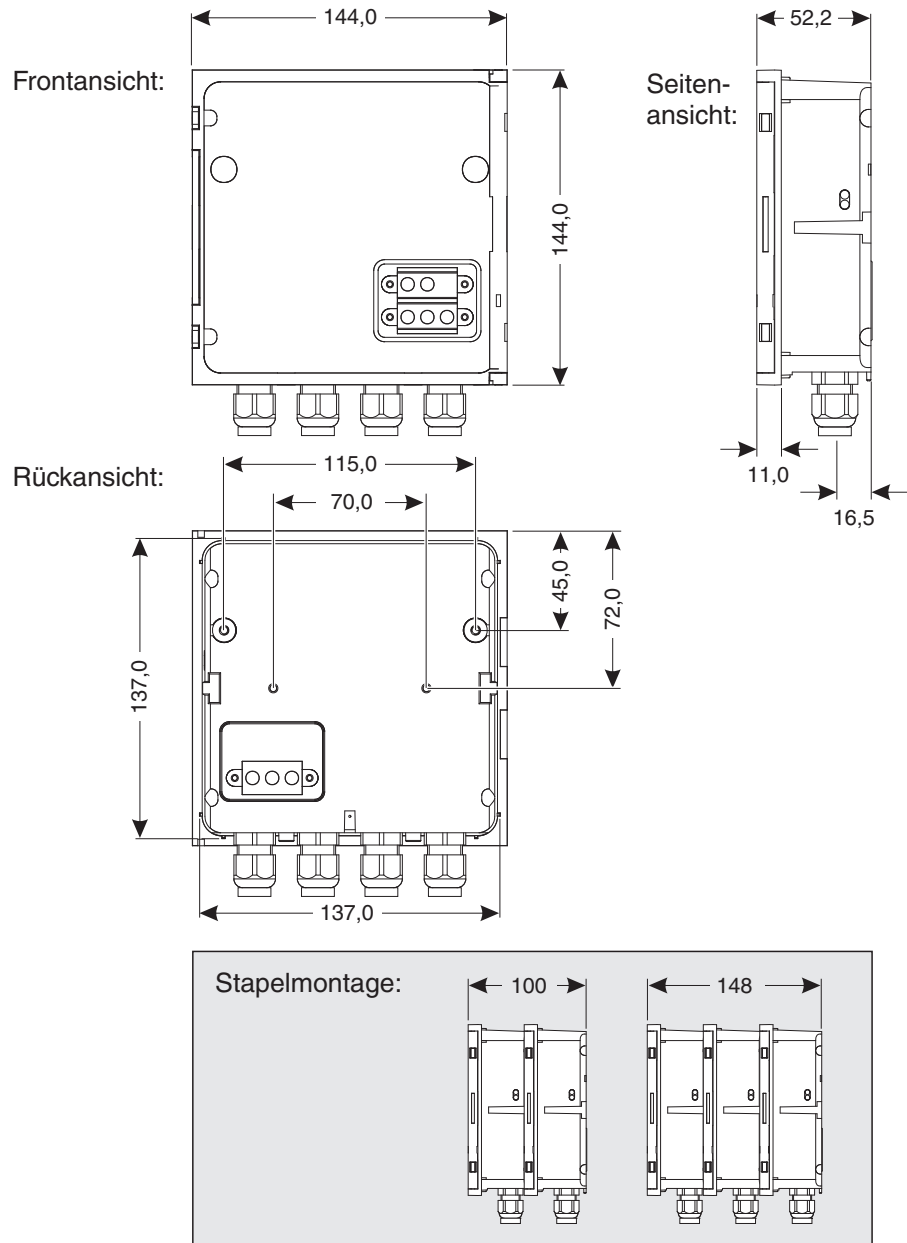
Maßzeichnung MIQ Modul (Maße in mm)
